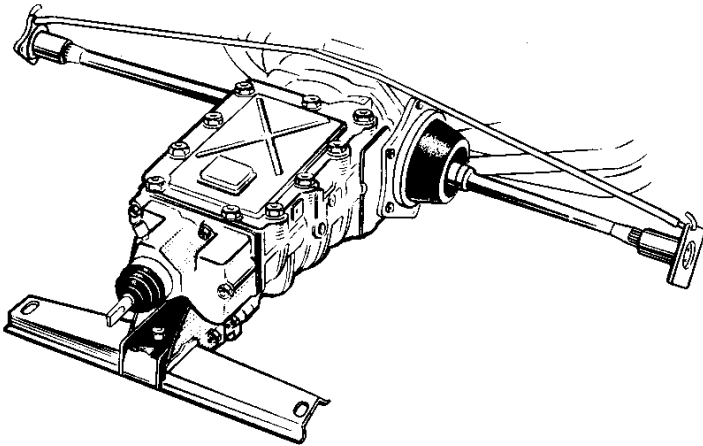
Закрепление полуосей при снятии и установке силового агрегата
